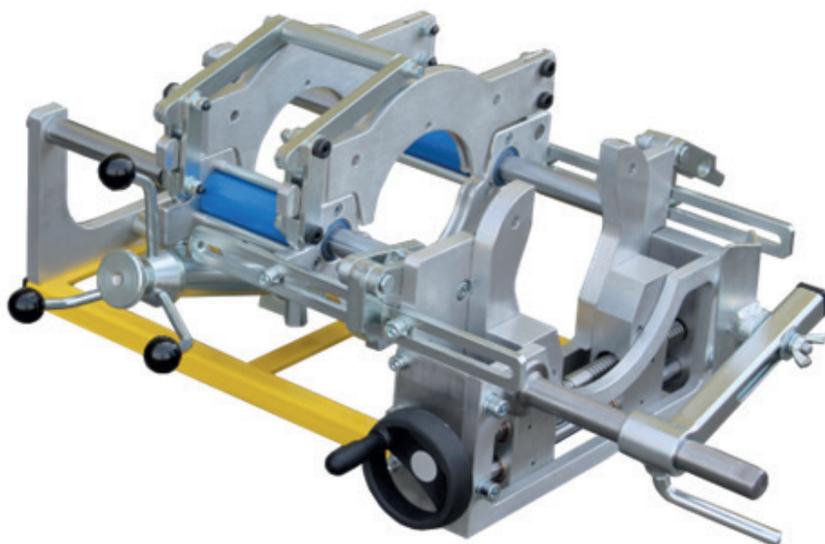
Сварочный аппарат с механическим центратором
